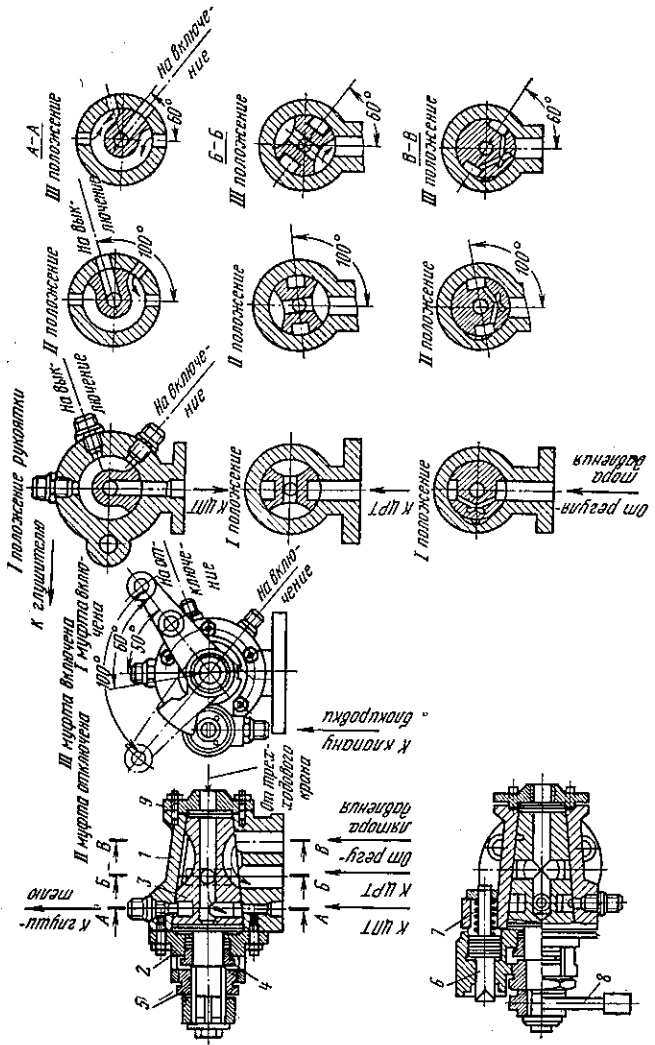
Кран механизма перестановки немодернизированной подъемной машины НКМЗ: 1 — корпус; 2 и 9 — крышки; 3 — пробка; 4 — нажимная гайка; 5 — регулировочная гайка; 6 — золотниковый упор; 7 — пружина; 8 — рычаг
